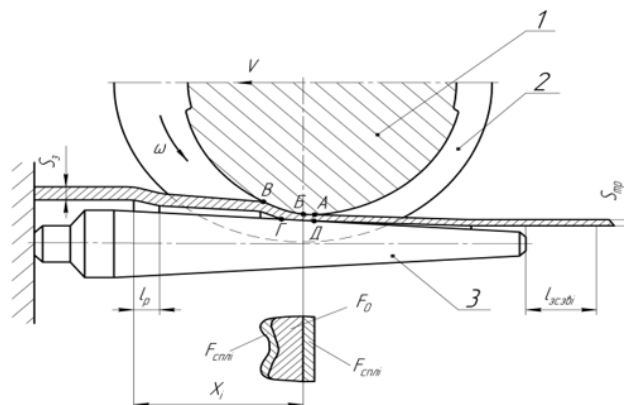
Схема сумарного та миттєвого осередку деформації при деформуванні труби - заготовки зворотним ходом кліті: 1- валок; 2 - річка валка; 3 - нерухома оправка; $S_з$ - товщина стінки труби-заготовки; $S_{тр}$ - товщина стінки прокатої труби; АБВГД- миттєвий осередок деформації; V - поступова швидкість валка; ω - кутова швидкість валка; $l_{зсзв}$ - лінійний зсув переднього торця труби; l_p - довжина зони редукування; F_o - горизонтальна проекція площі контакту річка валка з трубою, що деформується; $F_{спл}$ - площа збільшеної частини площі контакту річка валка з трубою за рахунок сплюснення валка; X_i - довжина від початку деформованої труби-заготовки до положення валка і [2].
